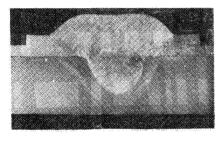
Макрошлиф соединений, выполненного дуговой точечной сваркой с принудительным несквозным проплавлением и формованием
